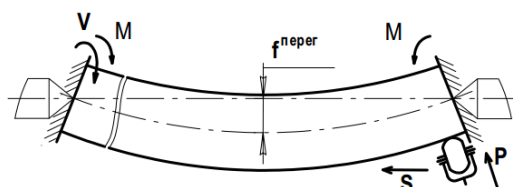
Схема правки ППД вращающейся упругодеформированной заготовки
